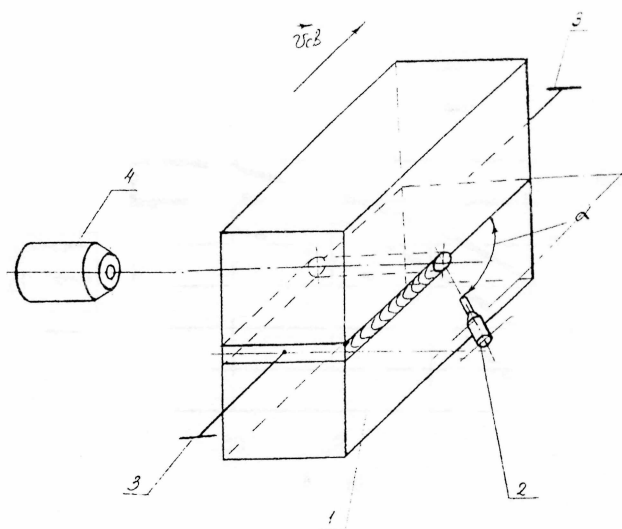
Схема двусторонней сварки: 1 - свариваемое изделие; 2- горелка для дуговой сварки; 3 - заземления; 4 - электронно-лучевая пушка;  $\alpha$  - угол наклона оси горелки.
